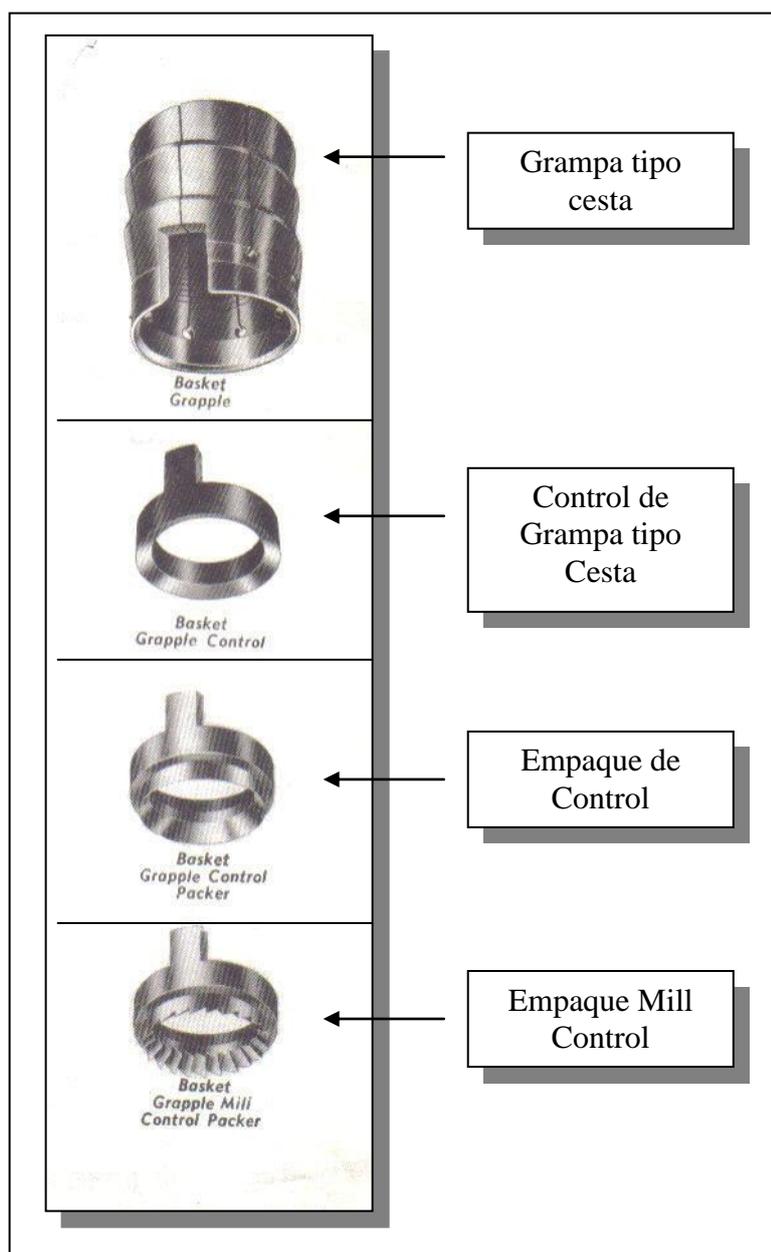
Grampa tipo cesta y empaques, fuente: Bowen Fishing Tools Technical Manual No.1150
